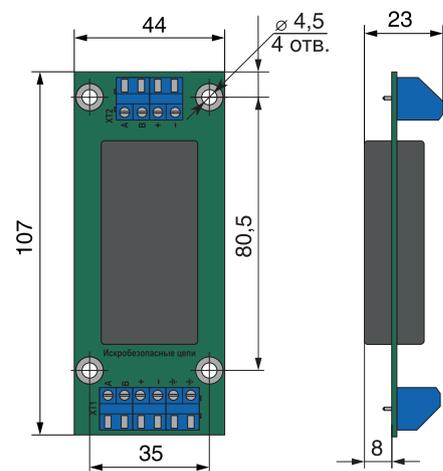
Габаритные размеры барьеров ЭНИ-БИС-113, 115, 118-Ex-01
